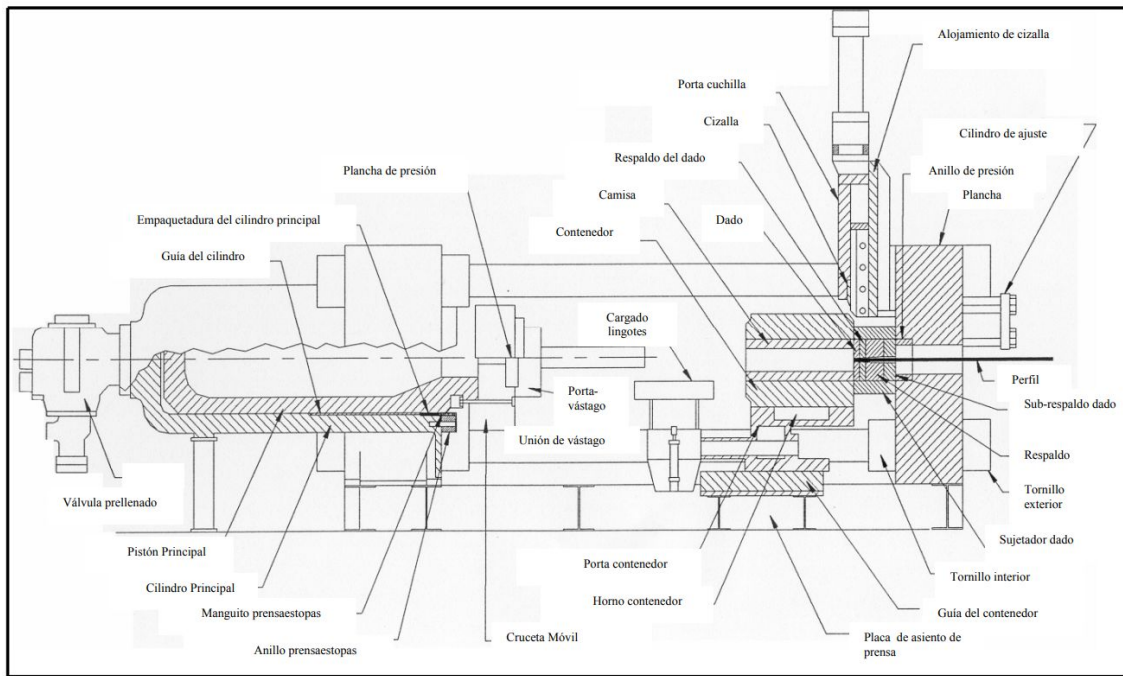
Equema de los componentes de una prensa extrusora de aluminio.
